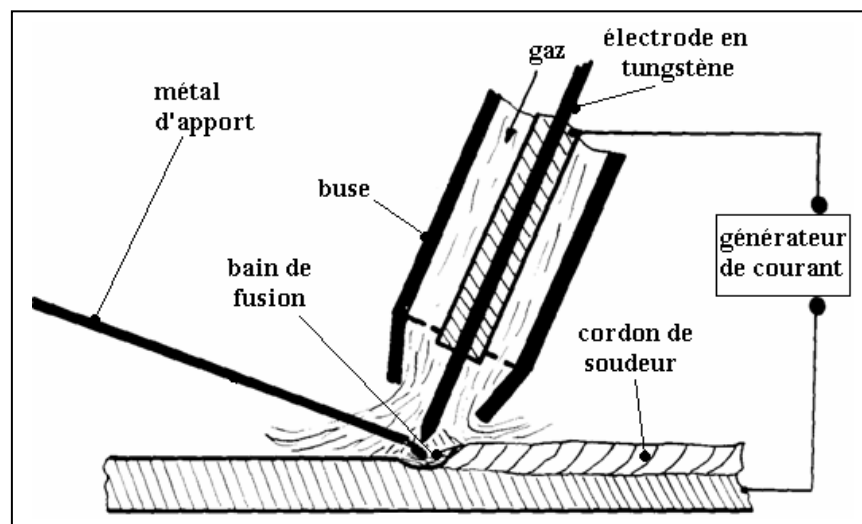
Schéma de principe du soudage TIG.
